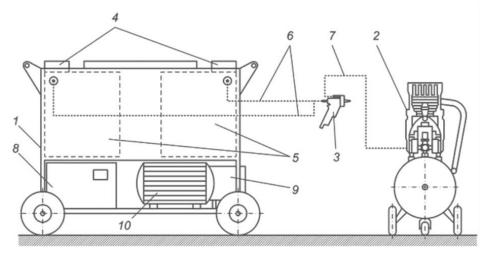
Схема установки для нанесения полиуретанового вяжущего 1 — установка для нанесения полиуретанового вяжущего; 2- компрессорная станция; 3 — пистолет-распылитель; 4 — заливочная горловина; 5 — емкость для компонента; 6 — шланг подачи компонента; 7 — шланг подачи воздуха; 8 — системы дозирования и термостатирования; 9 — система насосов для подачи компонентов; 10 — приводные двигатели
